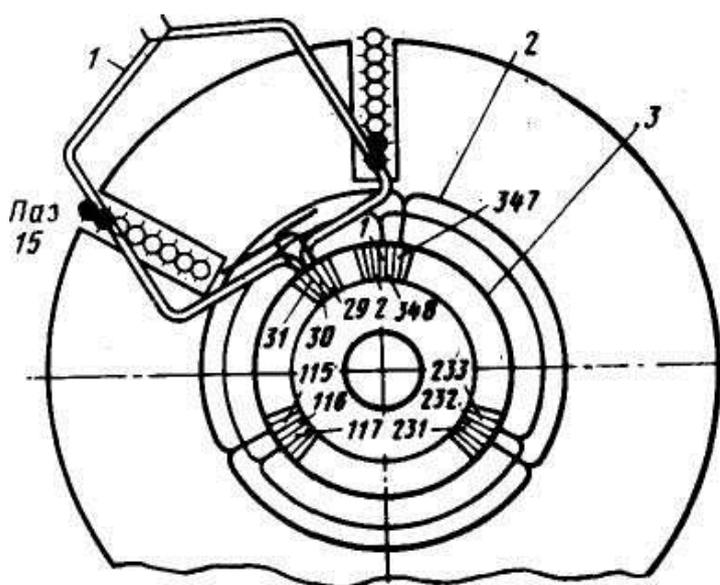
Схема соединения катушек якоря и уравнивателей с коллекторными пластинами тягового двигателя (вид со стороны коллектора) :
